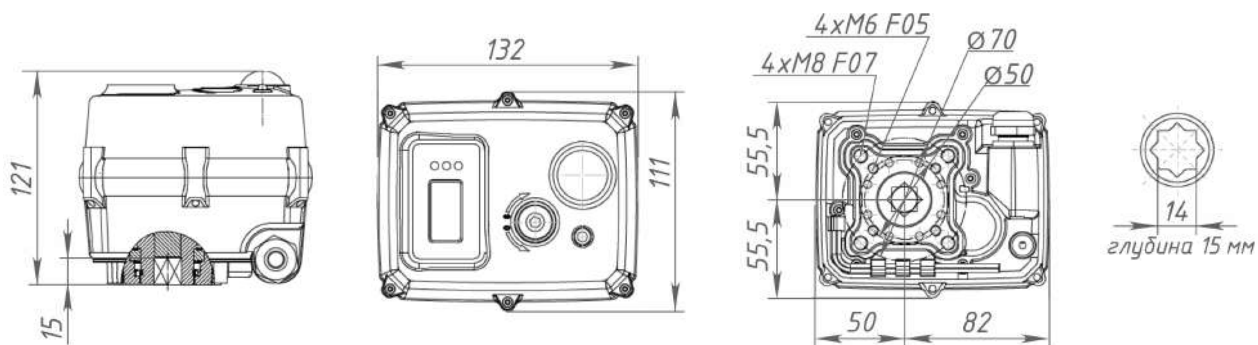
Габаритные размеры электроприводов Motorvalve серии Basic B50.
